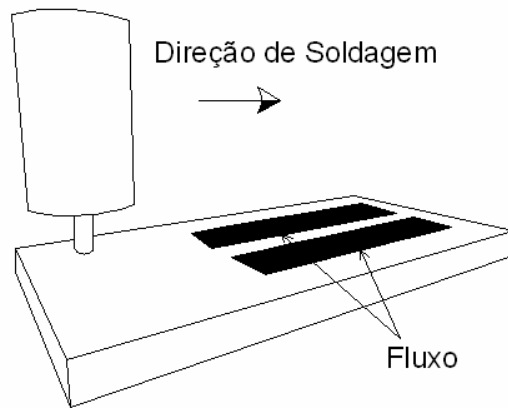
Soldagem FBTIG (SIRE *et al.*, 2002).
